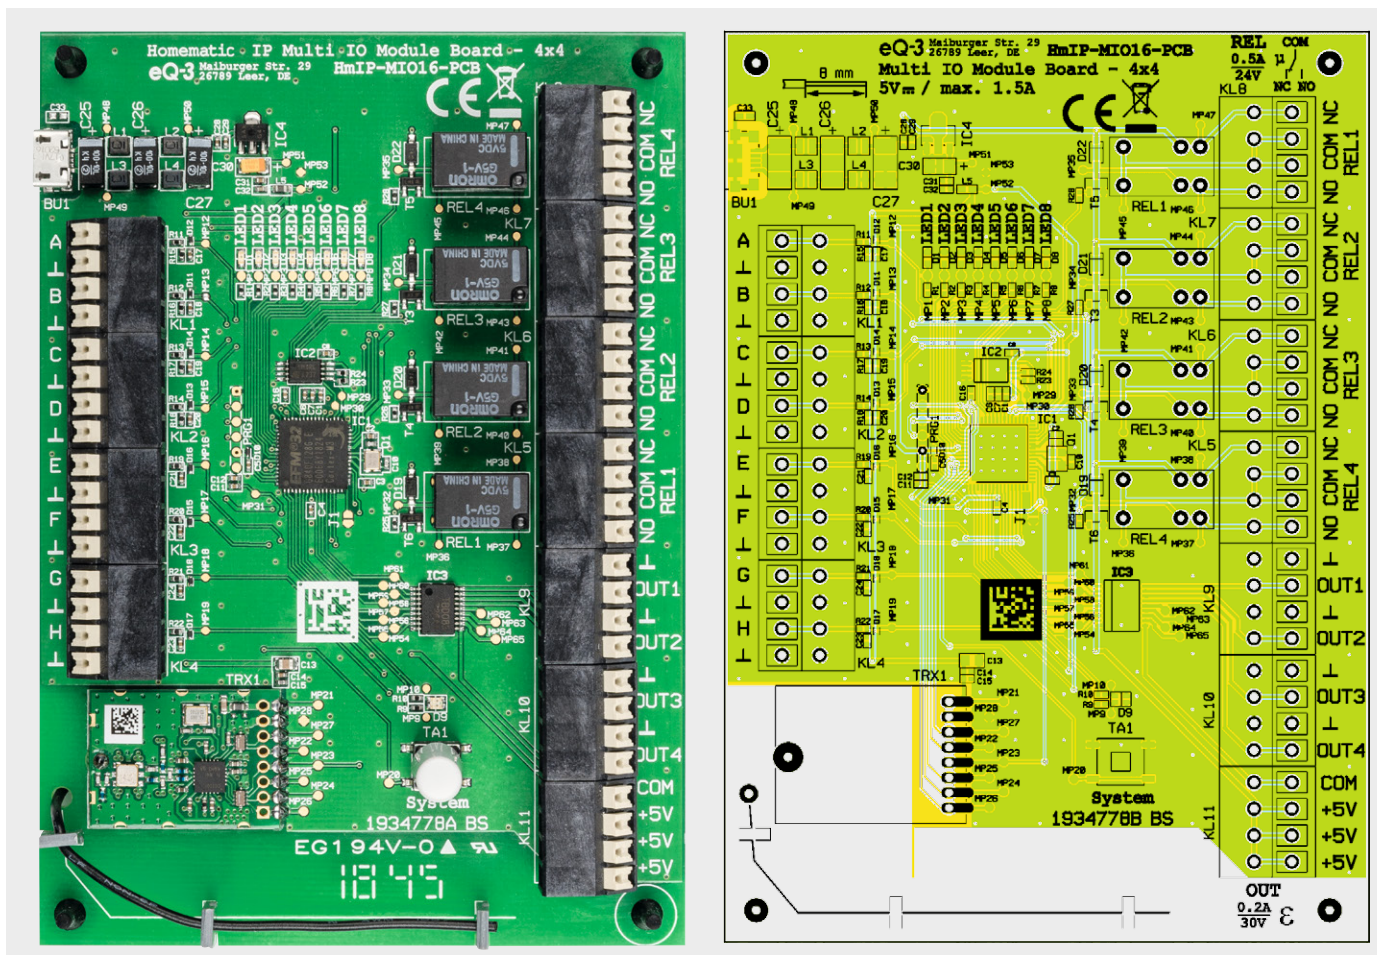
Die fertig bestückte Platine der HmIP-MIO16-PCB mit dem zugehörigen Bestückungsplan
